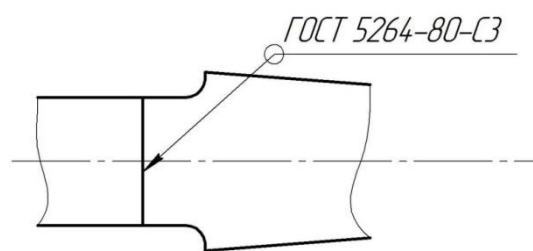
Эскиз сварного соединения рабочей части с хвостовиком
